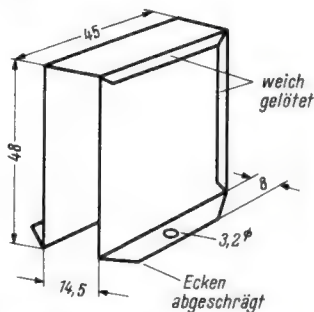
Halterung für Batteriesatz; Material: Weißblech 0,2 mm, die Hauptmaße sind Innenmaße
